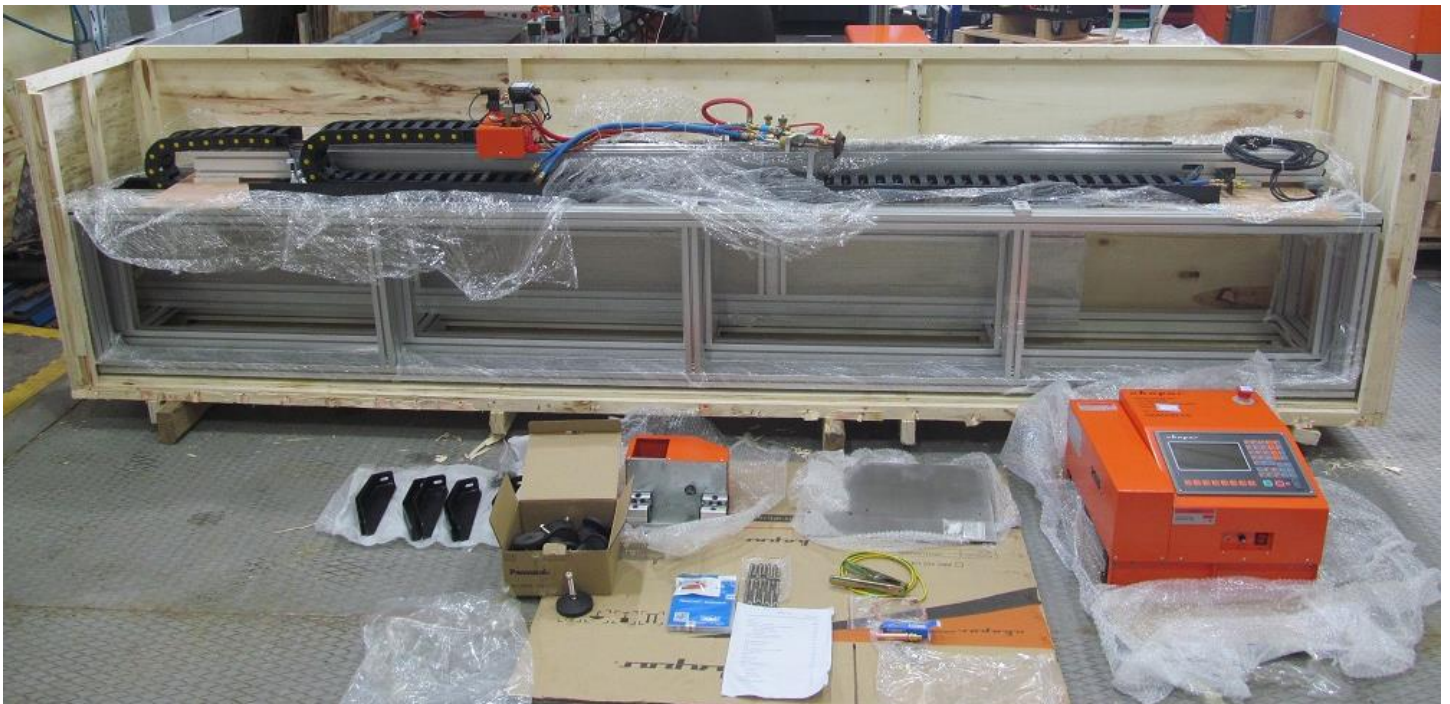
Общий вид станка и комплектующих со снятой боковой и верхней крышкой упаковки
